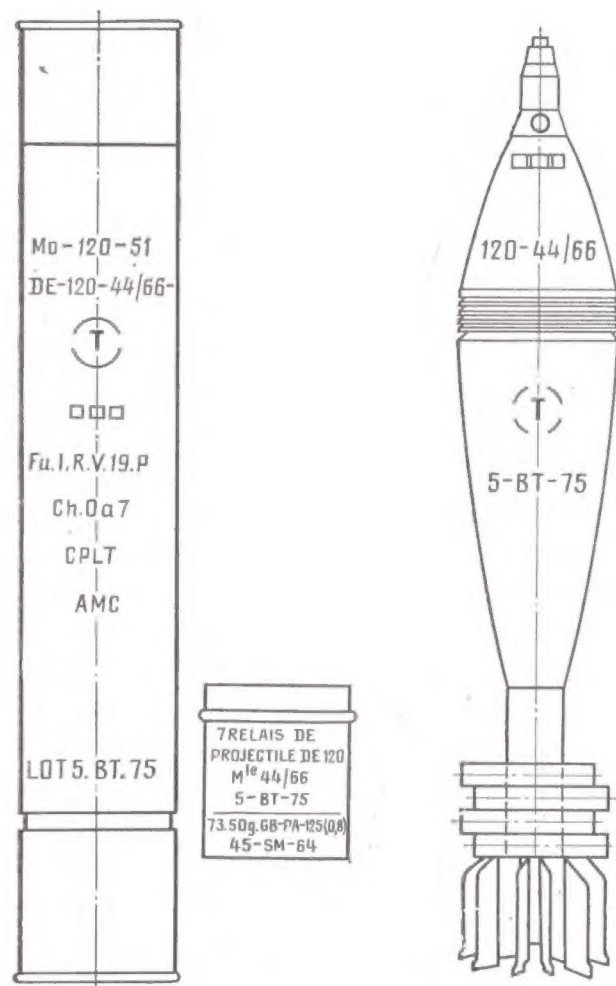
Образец маркировки мины M44/66, пенала для выстрела и упаковки для зарядов
